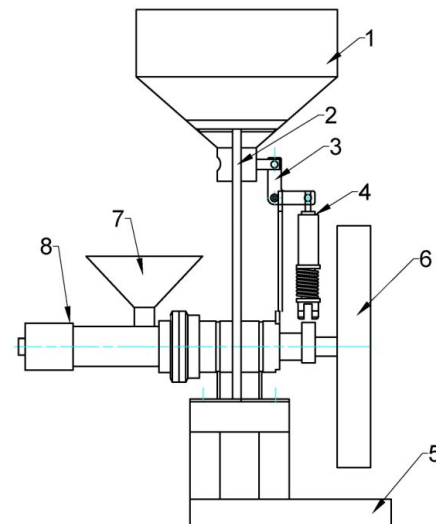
Экструдер ЭК-40: 1 - бункер; 2 - держатель бункера; 3 - механизм подачи смеси; 4 - толкатель; 5 - рама; 6 - ведомое колесо; 7 - приемная воронка; 8 - рабочая часть
